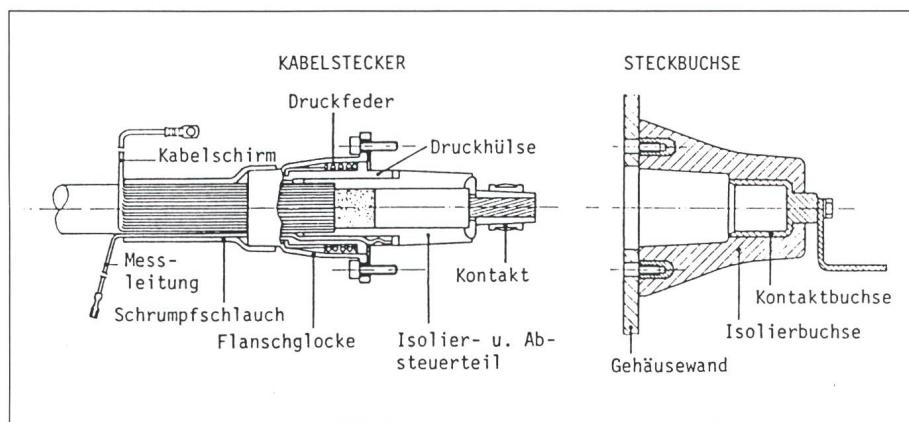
Innenkonus-Kabelstecksystem im Querschnitt
